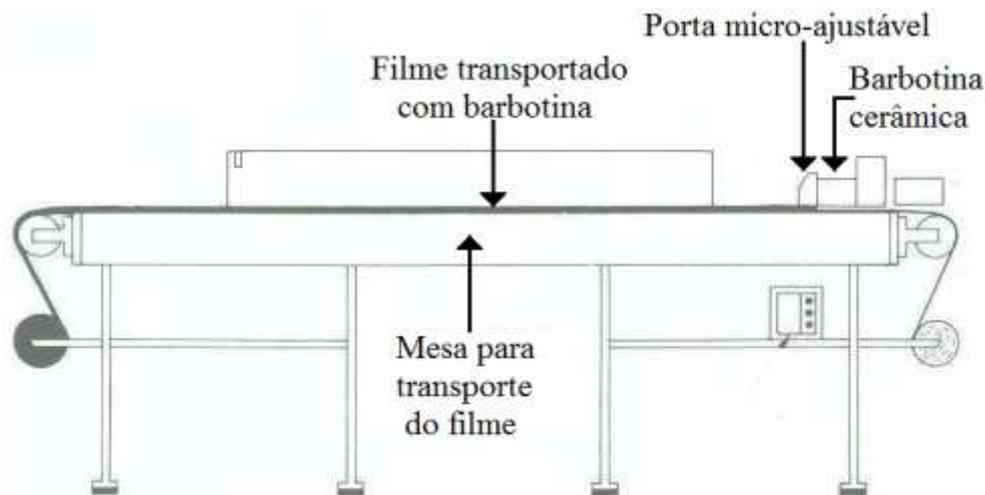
Equipamento de tape casting contínuo ⁽⁸⁾.
